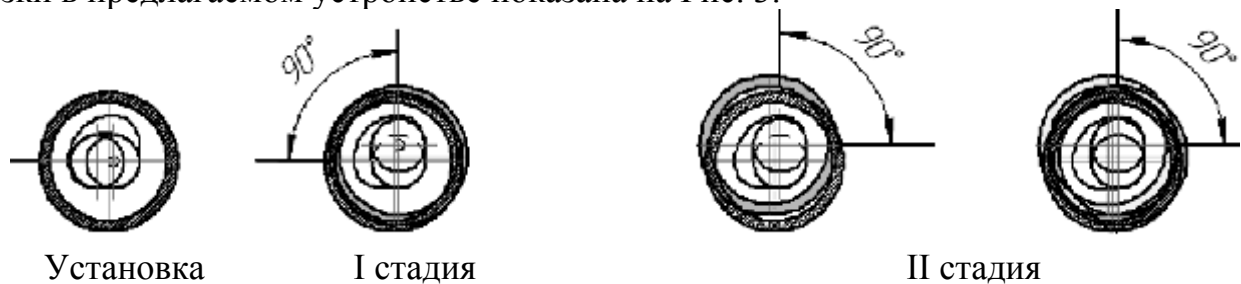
Стадии отрезки трубчатой заготовки сдвигом и кручением.
